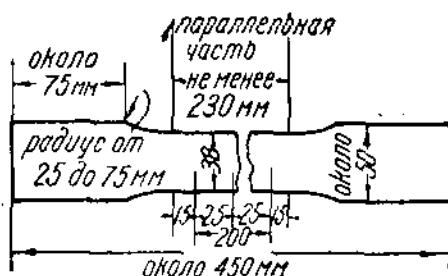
Стандартная форма образца для испытания на разрыв стальных листов, подлежащих горновой сварке или фланцеванию.
